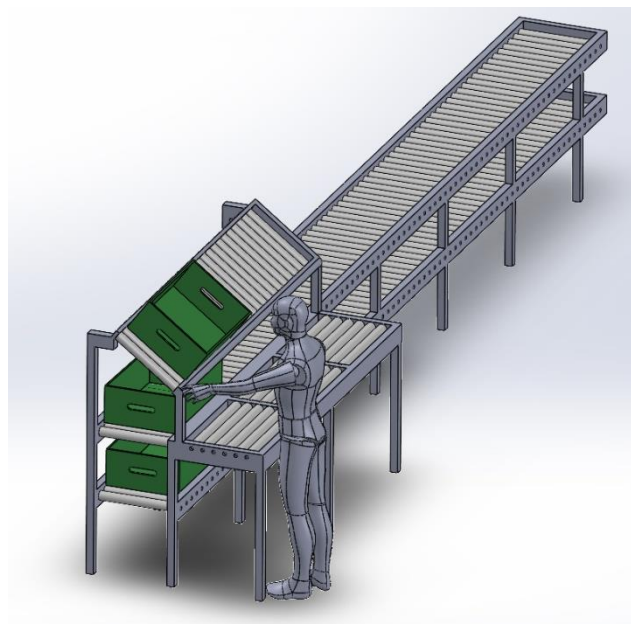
Solução para sistema de abastecimento da linha de embalagem B
